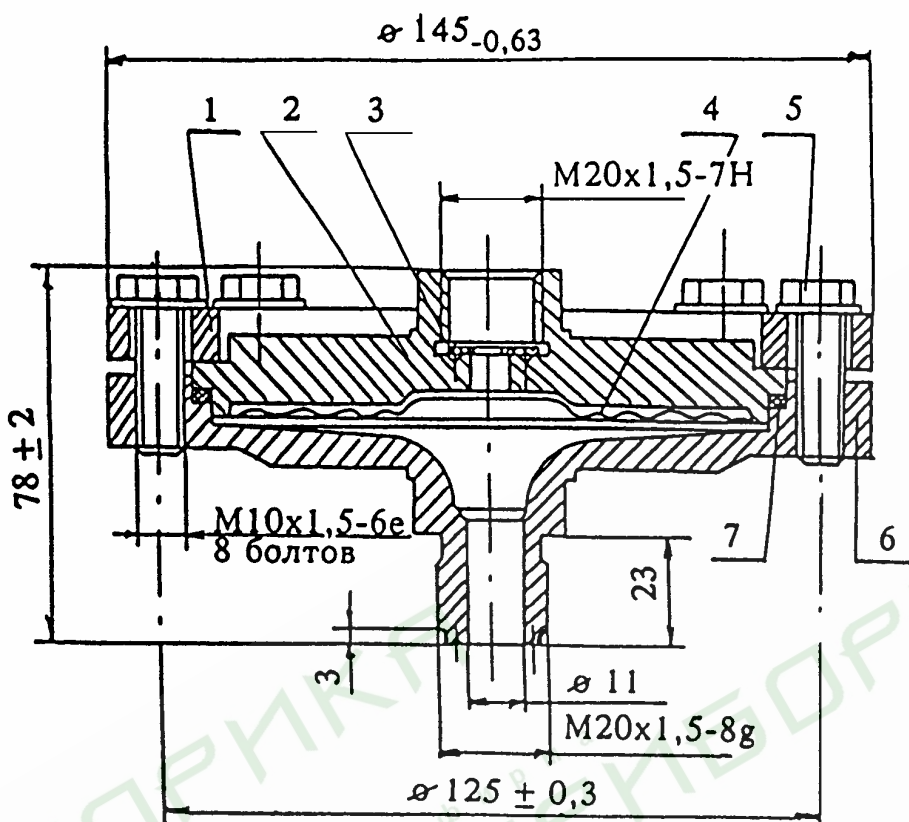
Габаритные и присоединительные размеры разделителя мембранного РМ модели 5497
